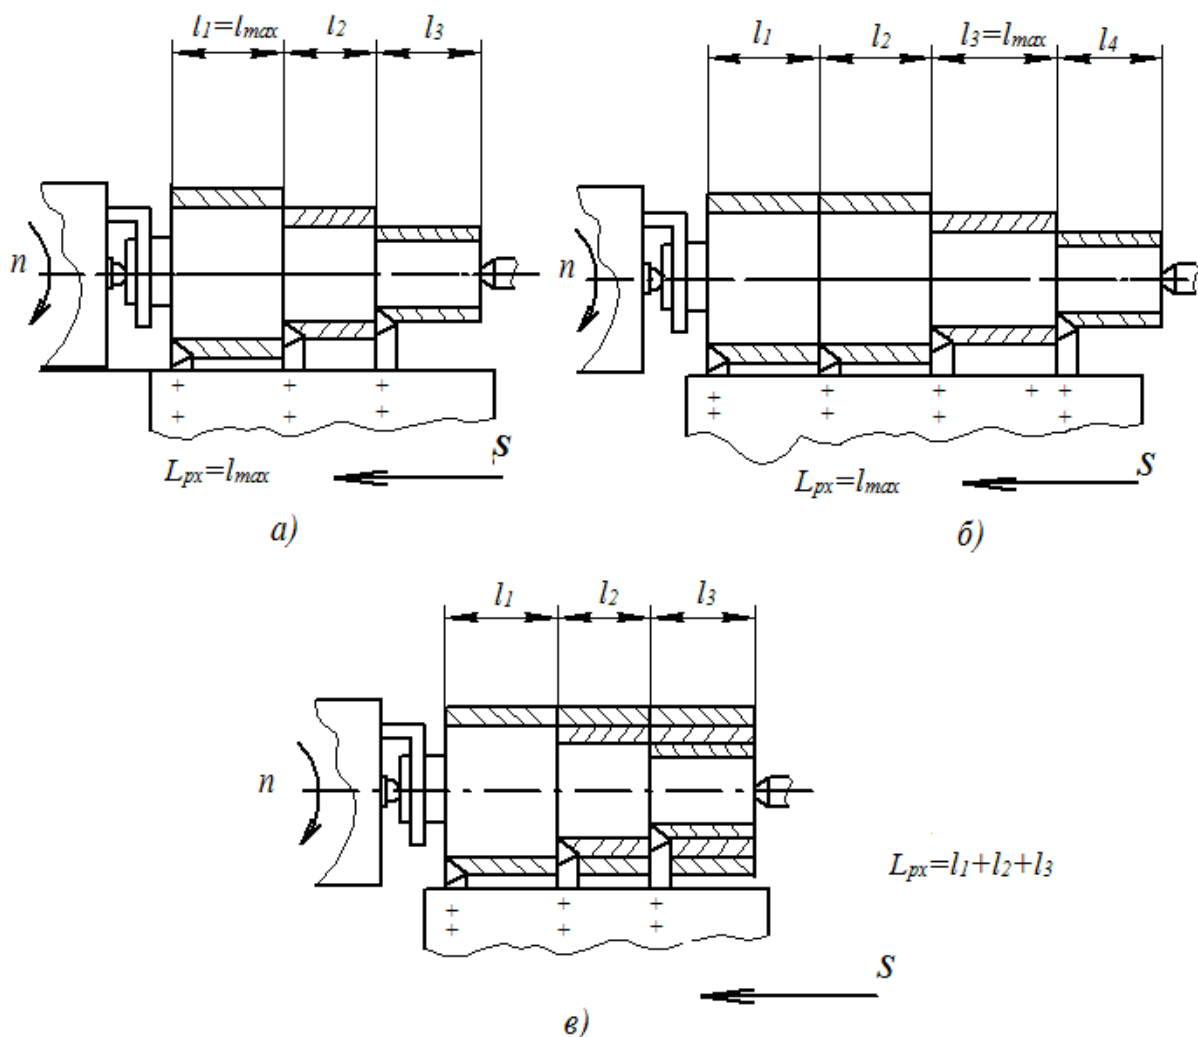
Три схеми обробки валів на багаторізцевих верстатах
